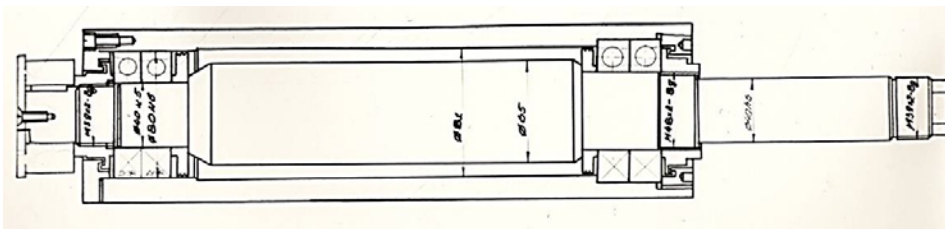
Разработанная конструкция консольного фрезерного шпиндельного узла
